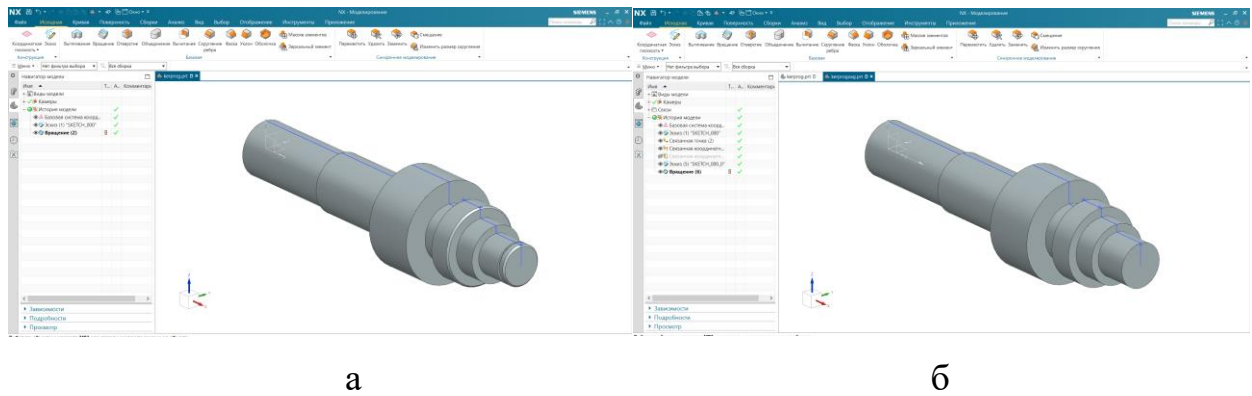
3D зображення деталі після токарної обробки (операція 025) (а)
